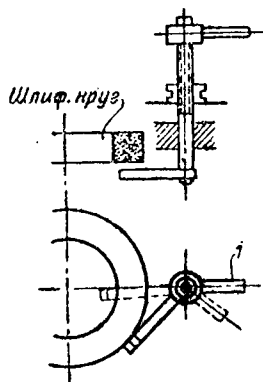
Схема приспособления для правки круга на станке 3732 МСЗ
